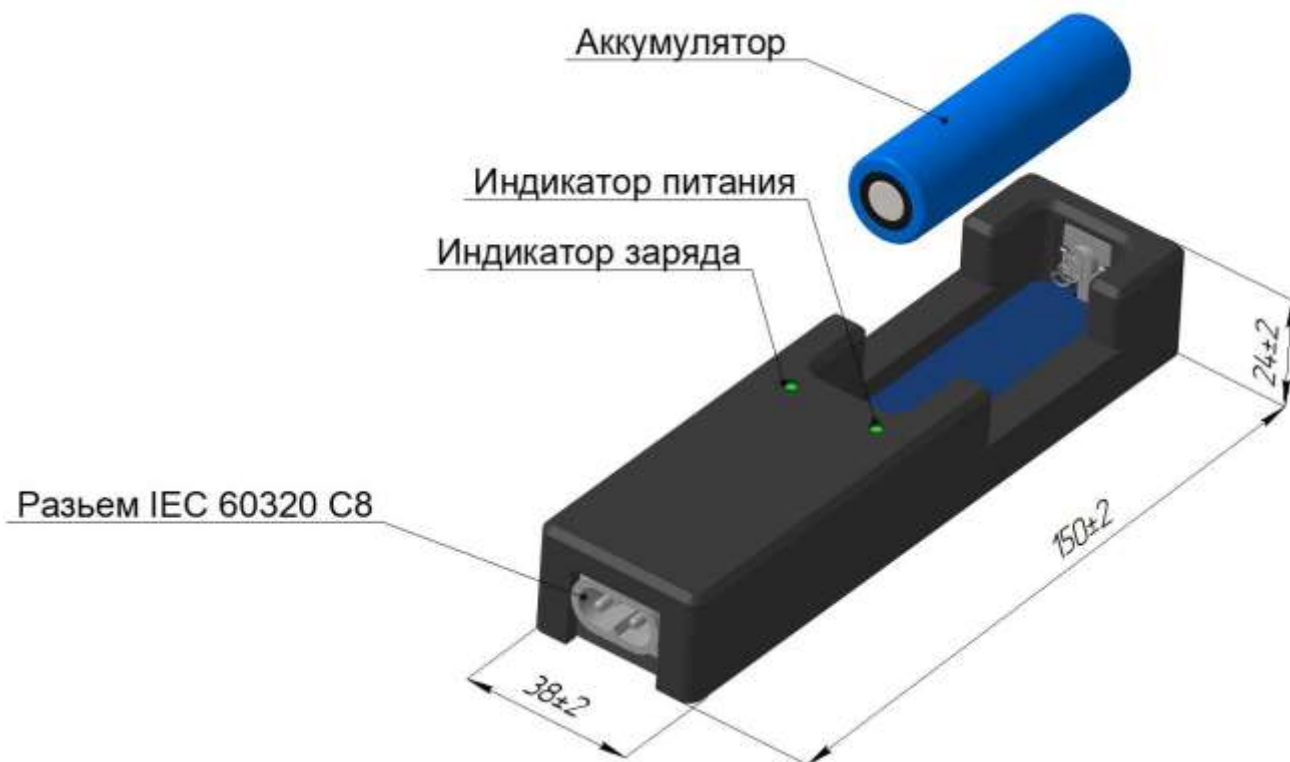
Внешний вид и габаритные размеры зарядного устройства
